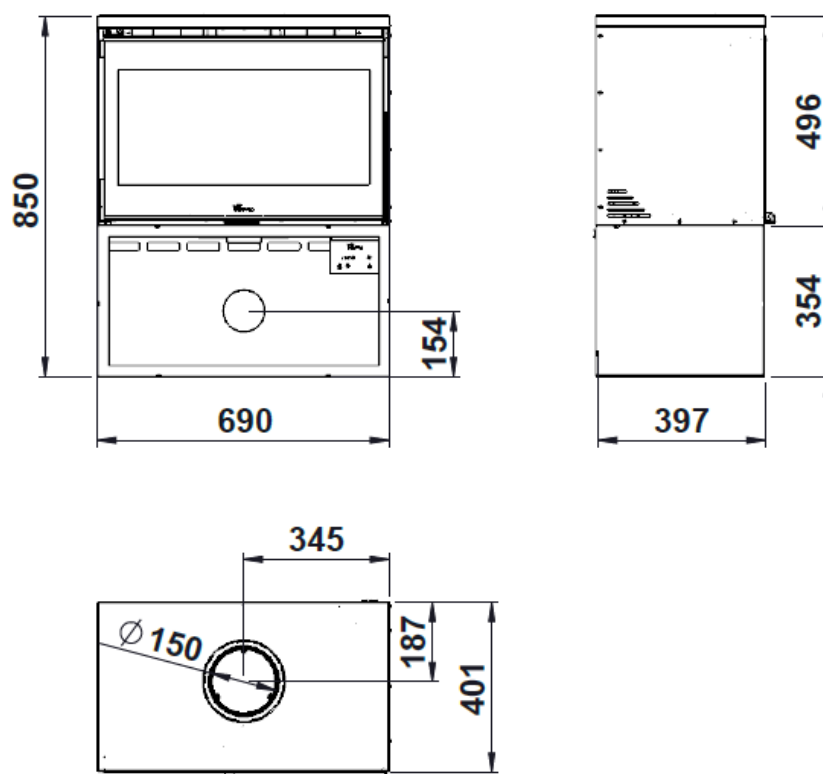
Dimensiones en mm del aparato PARIS 700
